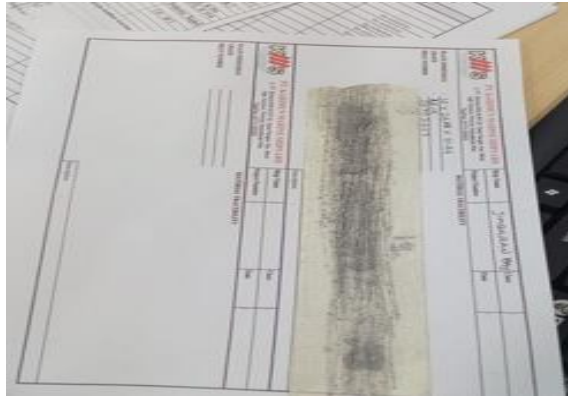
5 *Inspect Visual Weld Insert Plat
